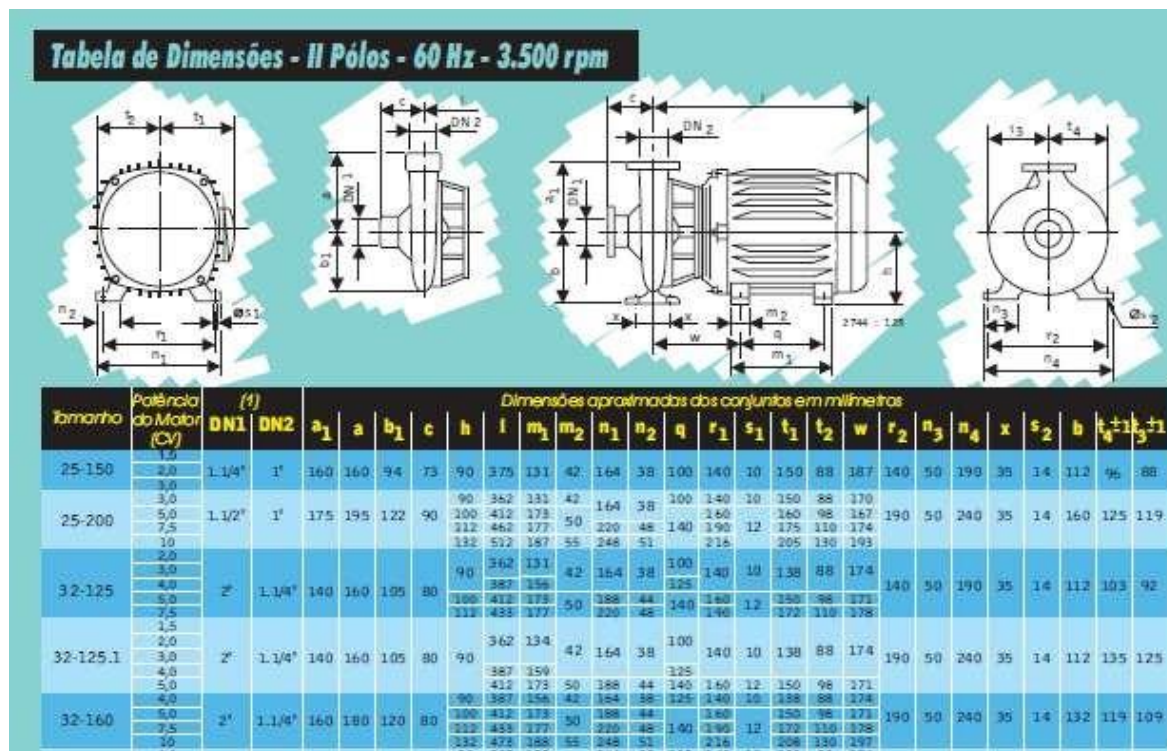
Dimensões do conjunto elevatório com motor de 7,50 CV
